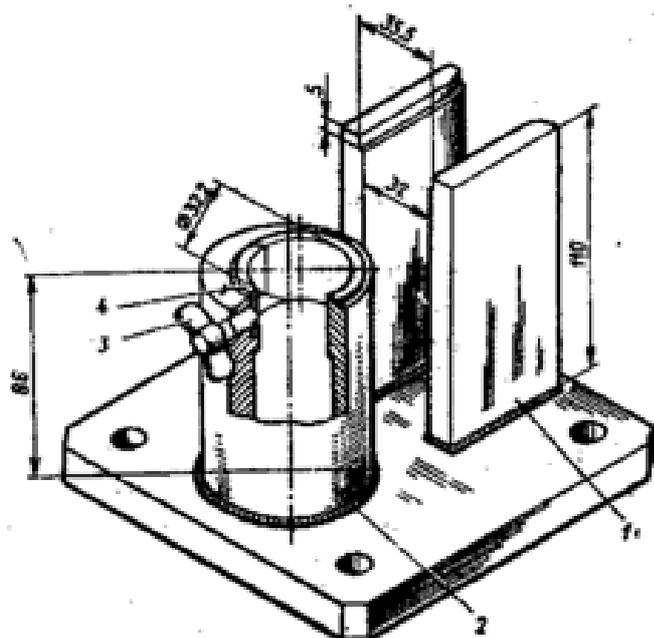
Приспособление M9832-337 для сборки ведомого вала и установки ведущего и ведомого валов: 1 - стойка для установки ведущего вала коробки передач; 2 - стойка для установки и сборки ведомого вала; 3 - зажим; 4 - сухарик зажима
